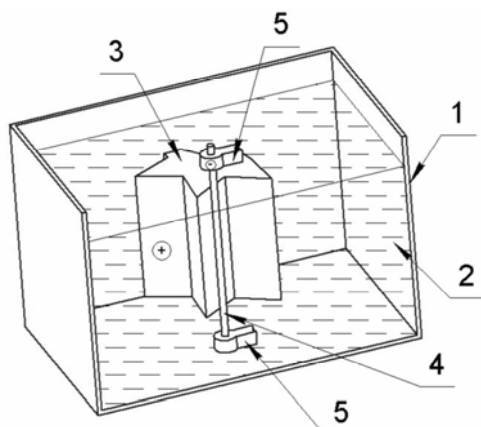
Схема реализации способа ЭХОПЭ: 1 – рабочая ванна станка; 2 – электролит; 3 – обрабатываемая заготовка; 4 – проволочный электрод; 5 – держатели проволочного электрода
